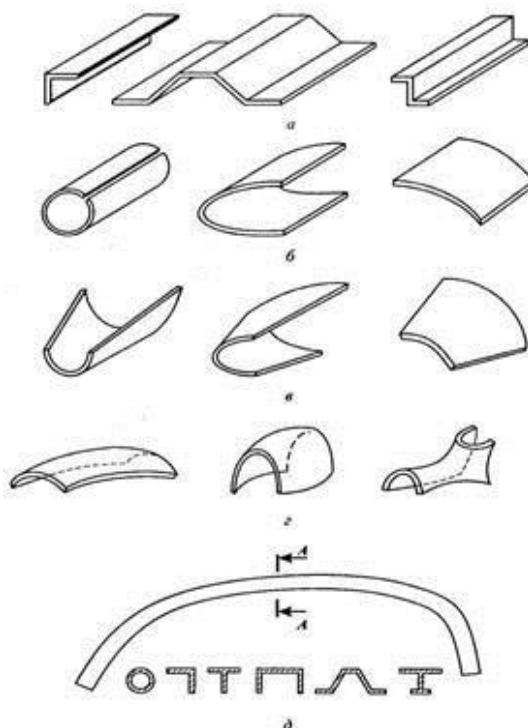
Типовые тонкостенные детали из листов и профилей: а - угловые детали из листового металла с прямолинейной образующей; б - цилиндрические детали из листового металла; в - конические детали из листового металла; г - выпуклые и выпукло-вогнутые детали из листового металла; д - криволинейные детали из профилей и труб
